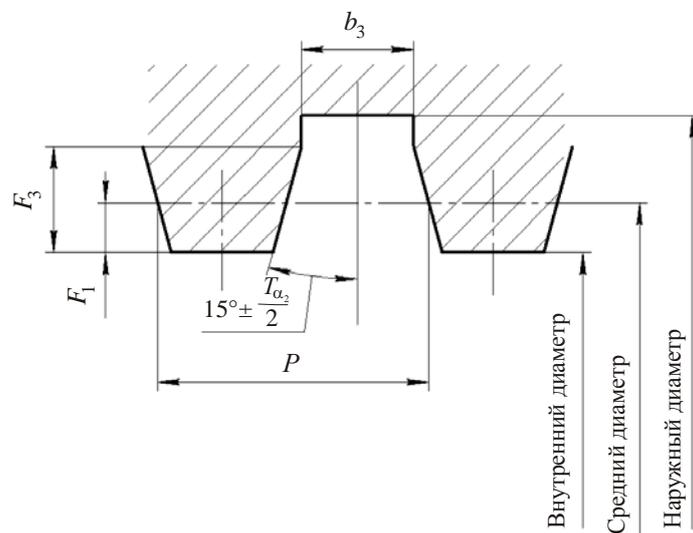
Укороченный профиль резьбы калибров-колец и скоб для контроля наружной трапецеидальной резьбы
